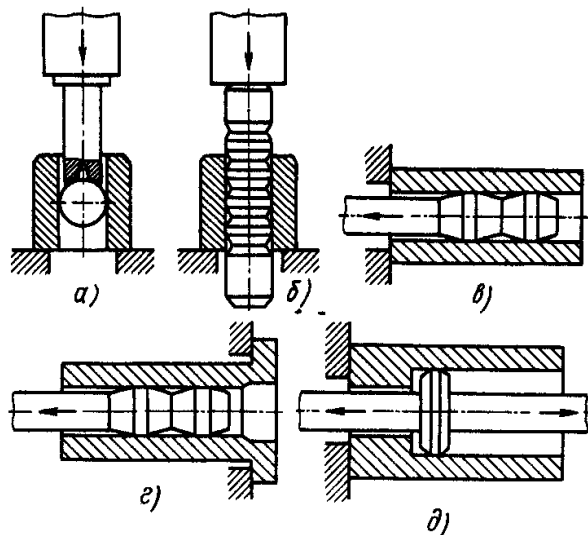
Схемы обработки отверстий: а и б – прошиванием с помощью шарика и оправки; в – со сжатием детали; г – с растяжением детали; д – при возвратно-поступательном ходе оправки
